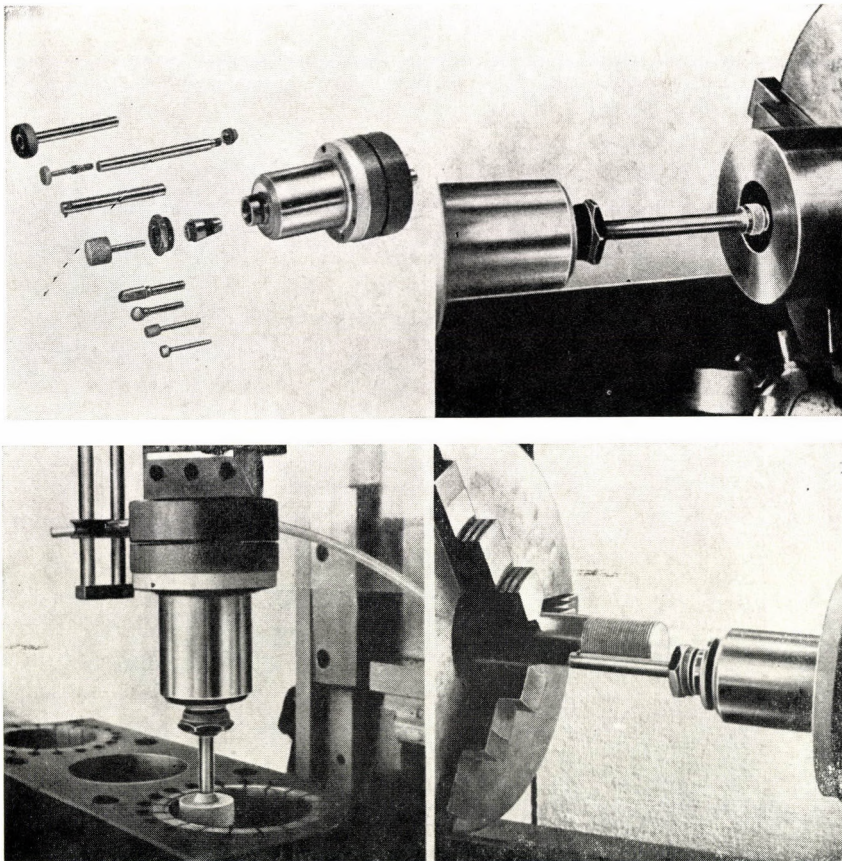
Montage und Anwendbarkeit des Turbo-Schleiffräasers auf Werkzeugmaschinen
